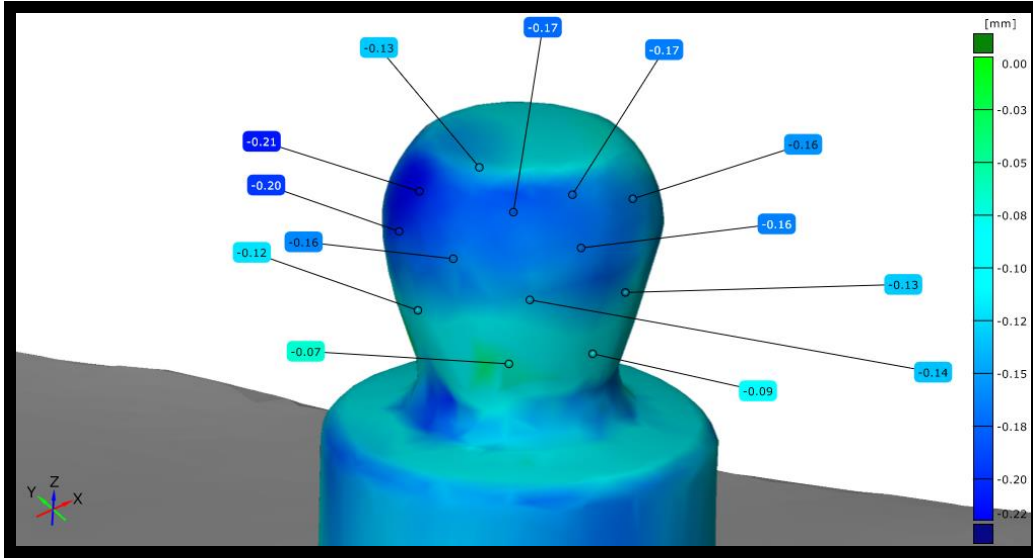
Siklus Deneyi Sonrası BİOH 5B abutment çapı (2.48 mm)
